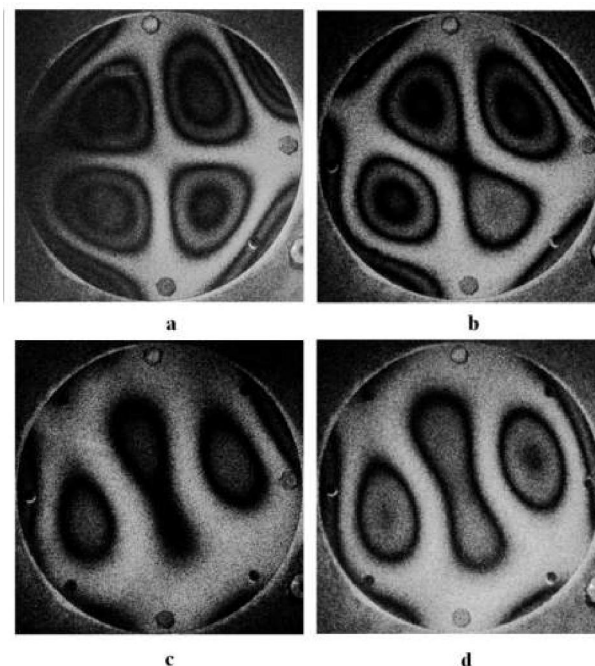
Изменение формы колебаний крышки группового резьбового соединения
